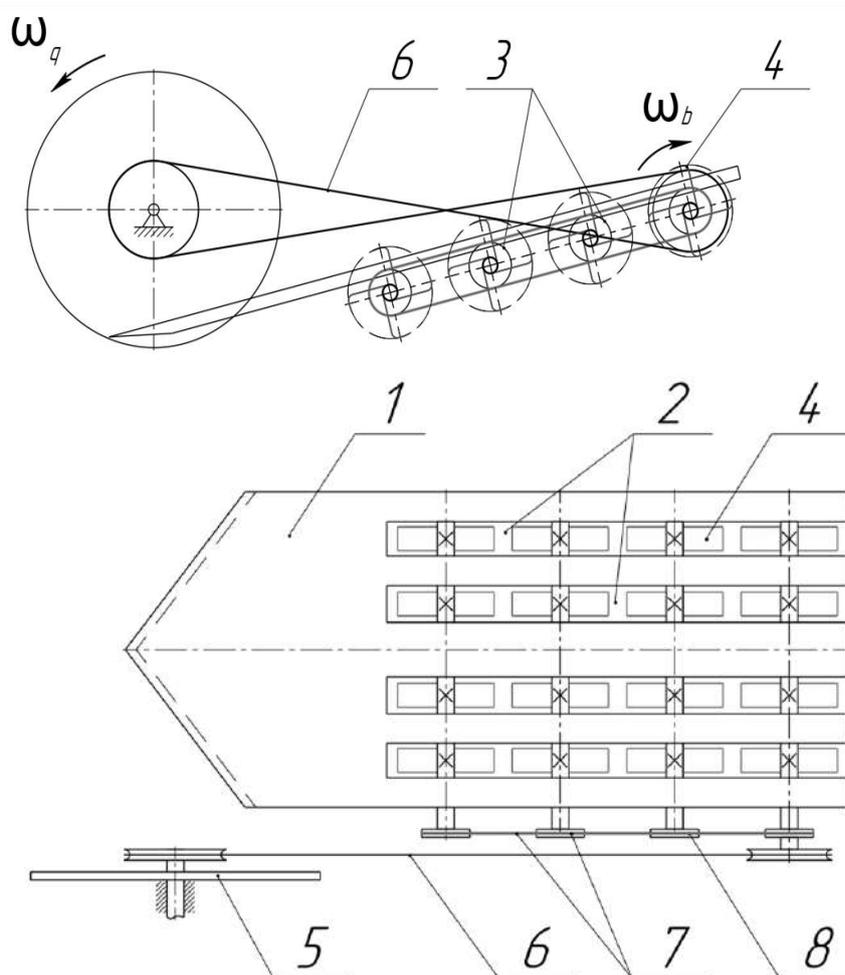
Схема подкапывающего лемеха с пассивной подрезающей частью и активной рабочей поверхностью.
